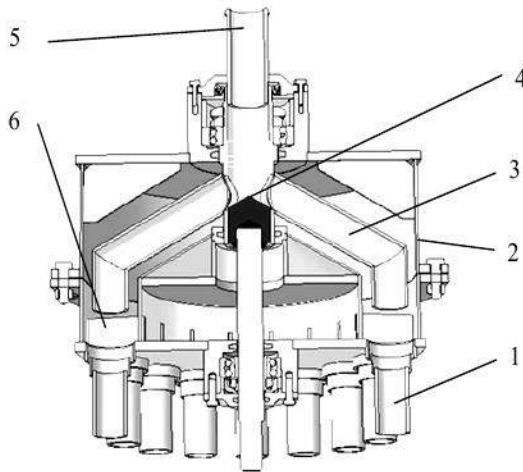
Розподільча головка: 1 - розвідний шланг; 2 - корпус; 3 - роздавальний патрубок; 4 - вал приводу роздавального патрубку; 5 - нагнітальний трубопровід; 6 – сопло
